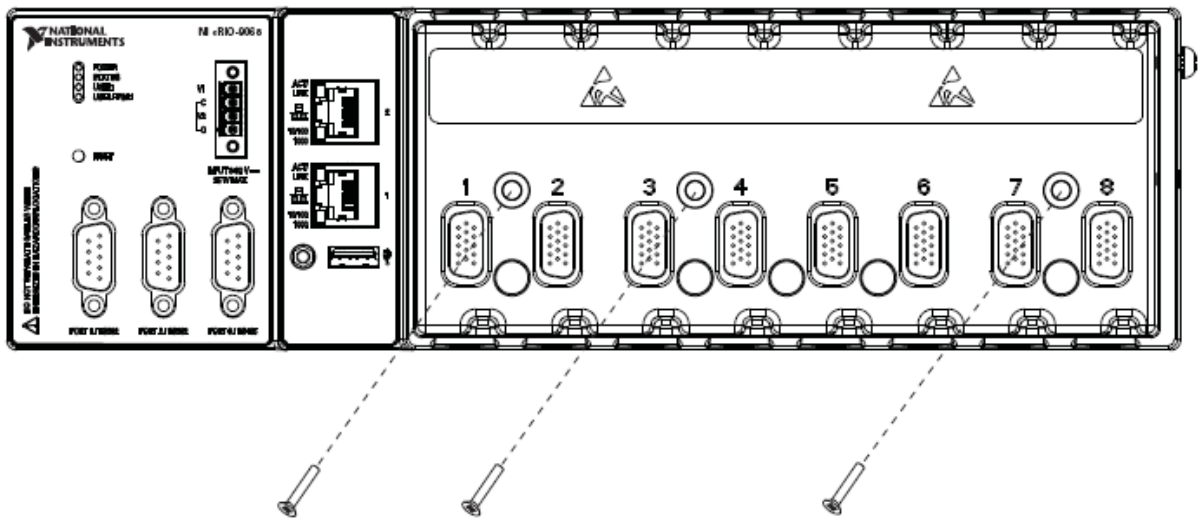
Установка cRIO-9068 на плоскую поверхность
